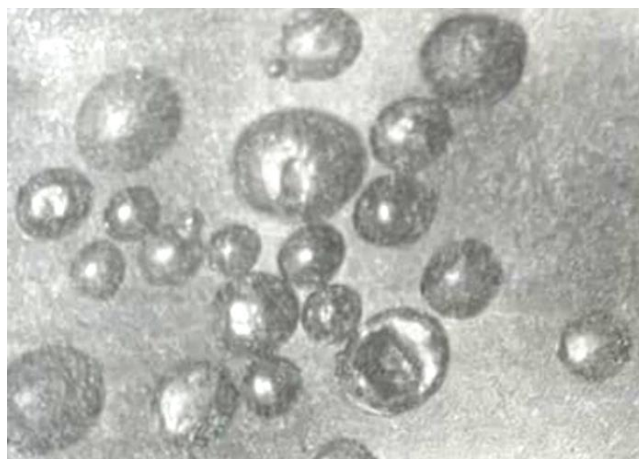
Капли электродного металла, извлеченные из шлаковой корки
